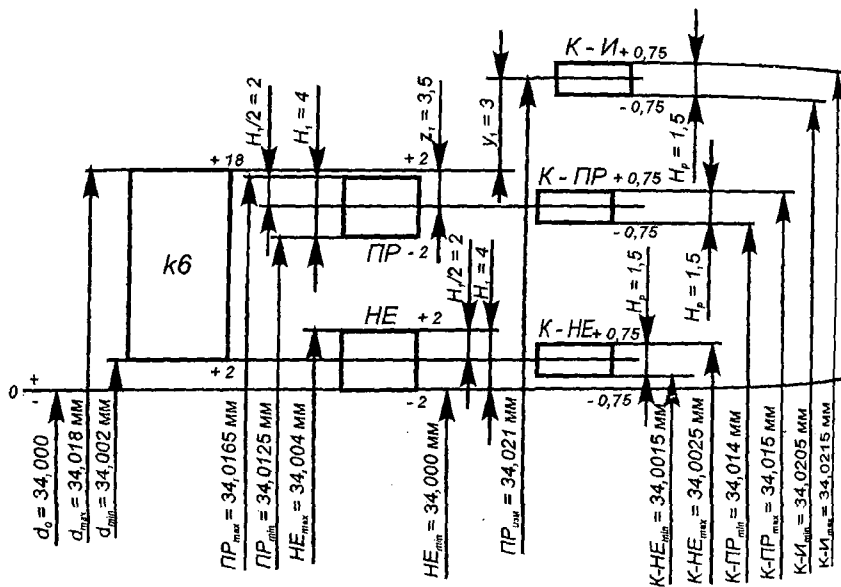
Схема расположения полей допусков калибров для контроля вала  $\varnothing 34k6$  и контрольных калибров
